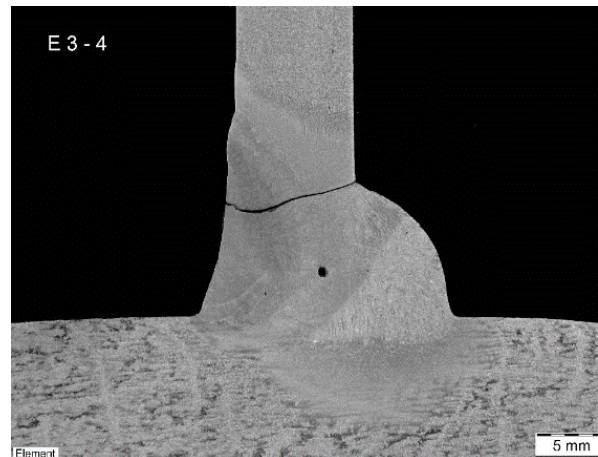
Schweißimperfektionen HV-Naht [21]
